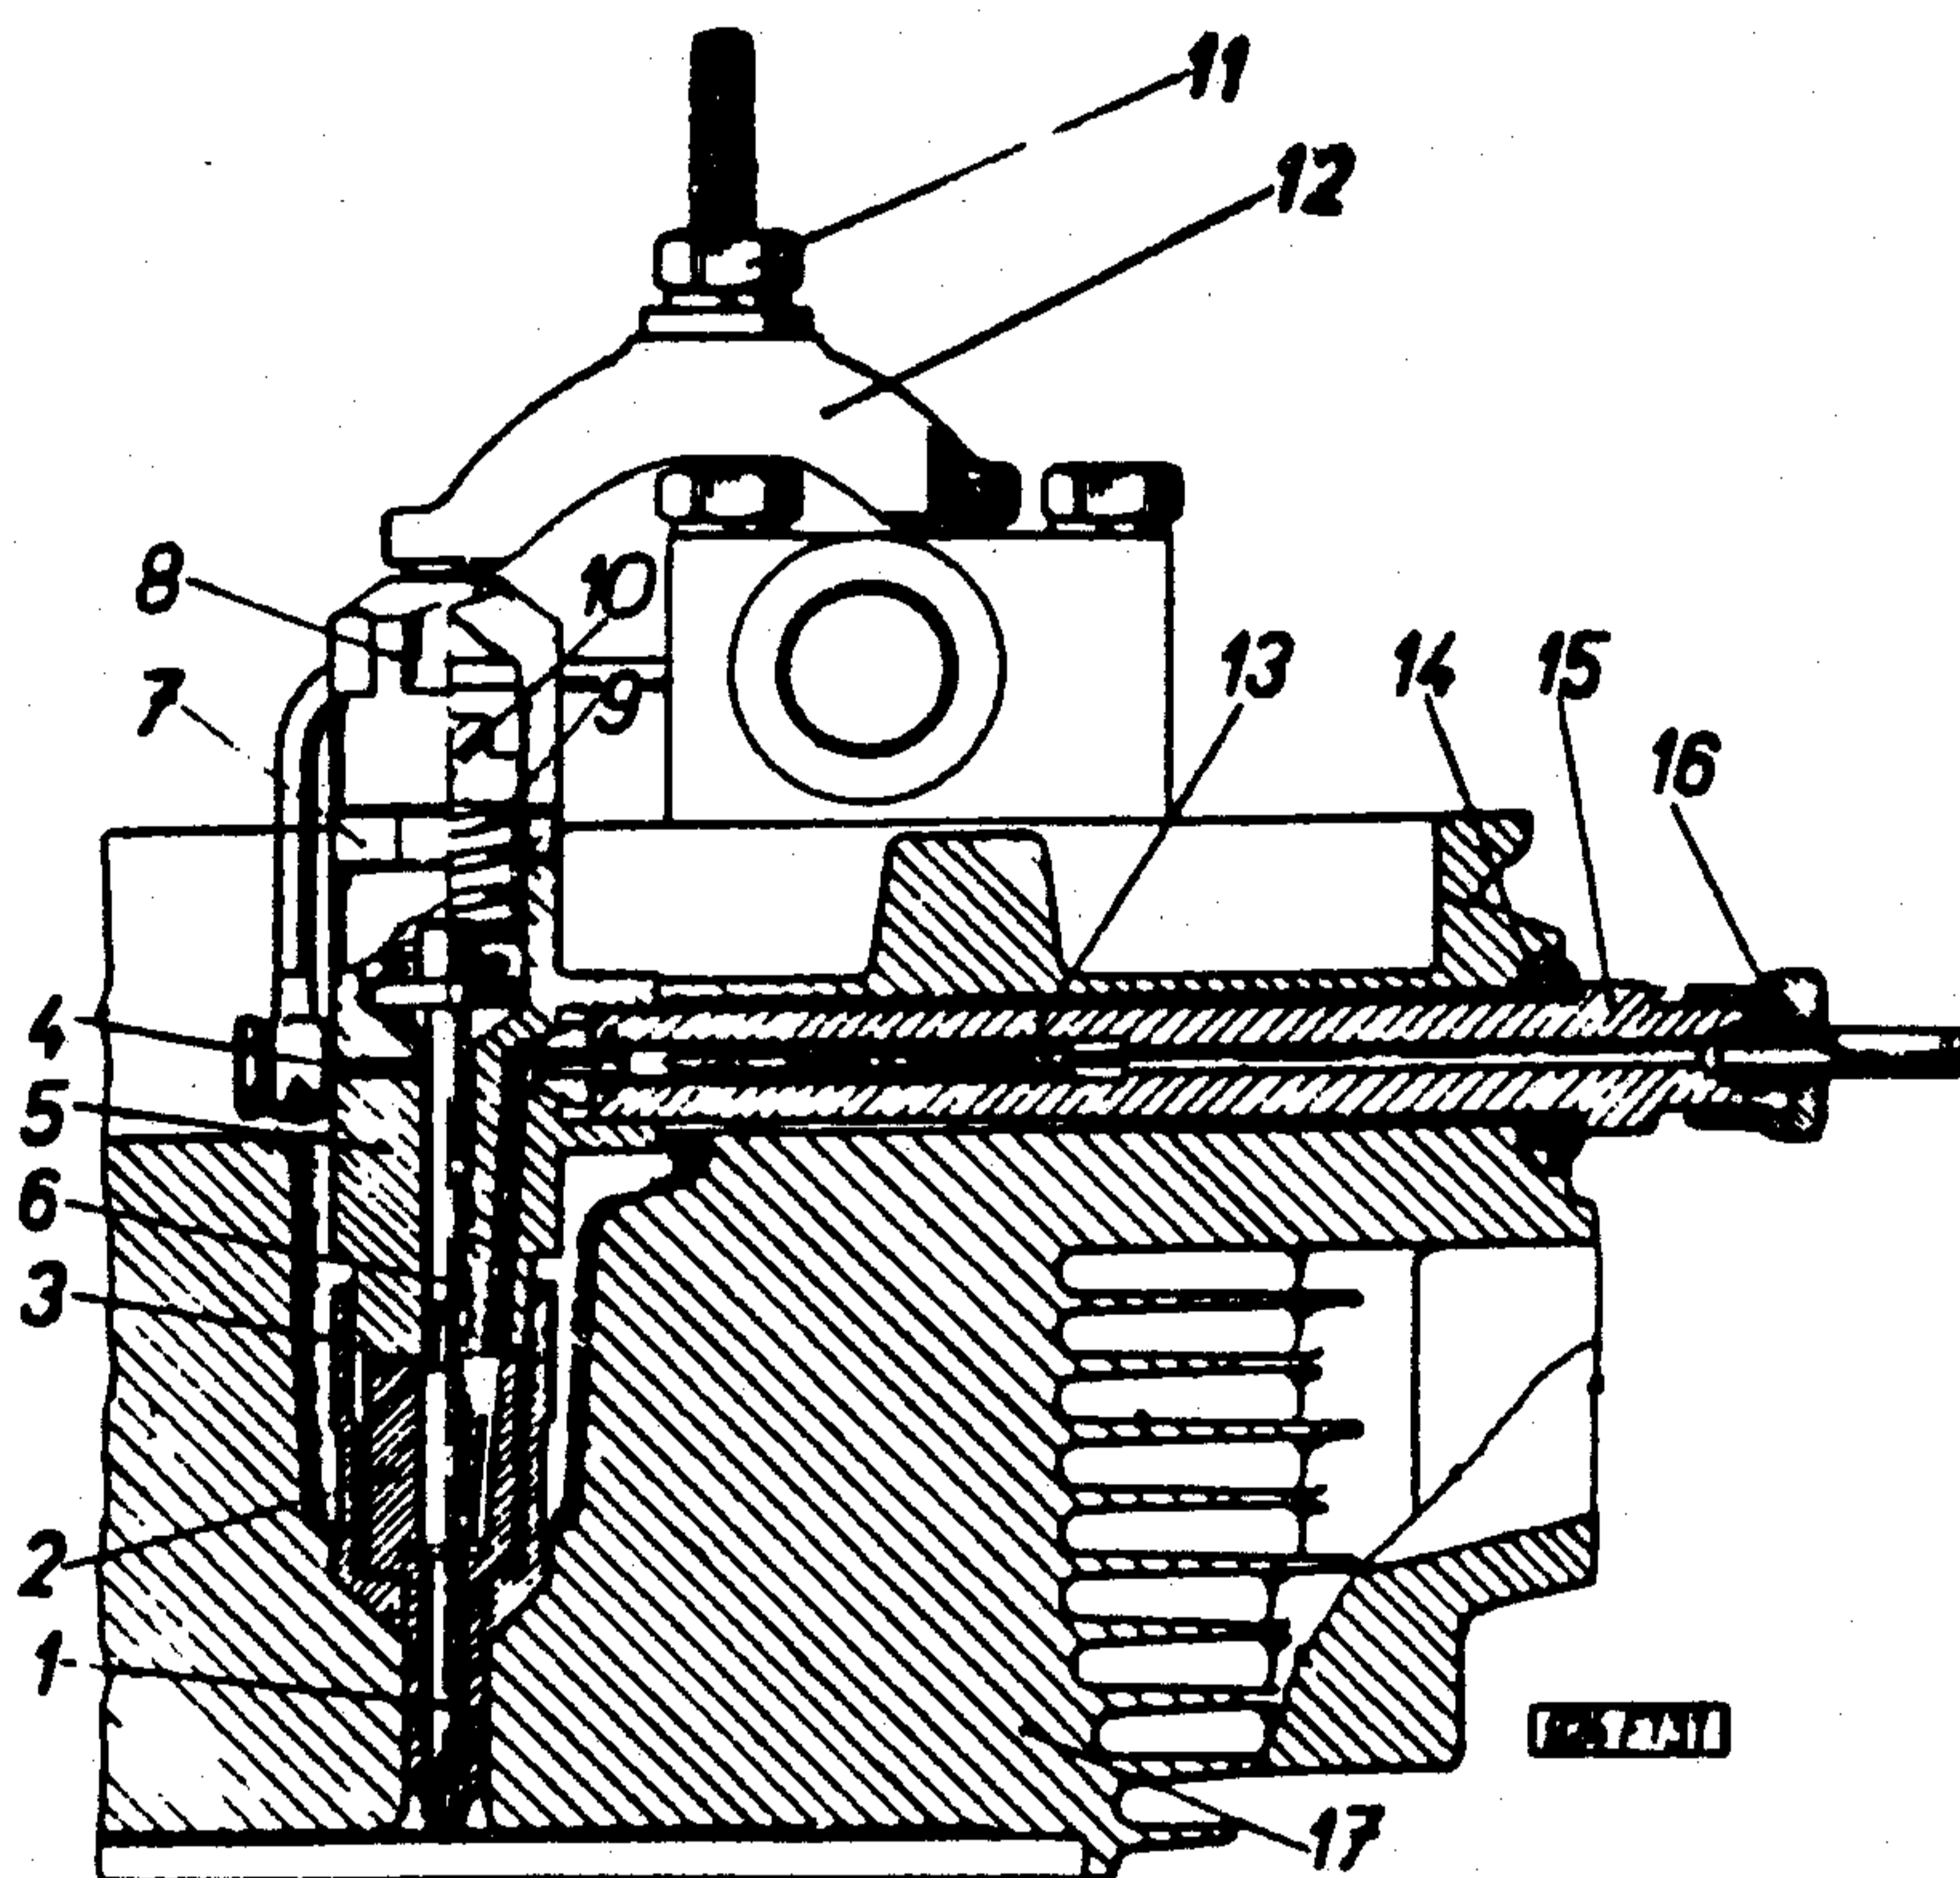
Einspritzventil MOTORPAL im Zylinderkopf
